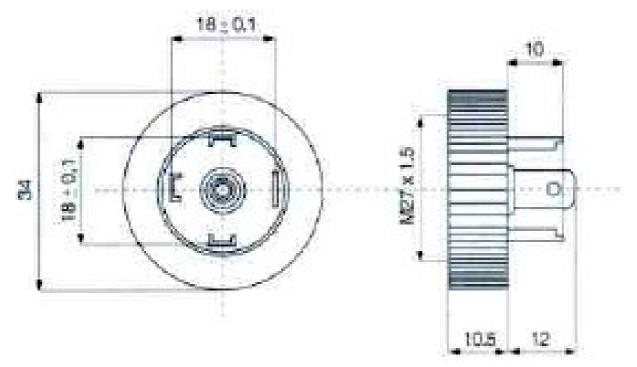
База для герморазъёма DIN 43650, форма А круглая (соединитель электрический ISO 4400) с тремя контактами плюс заземляющий контакт
